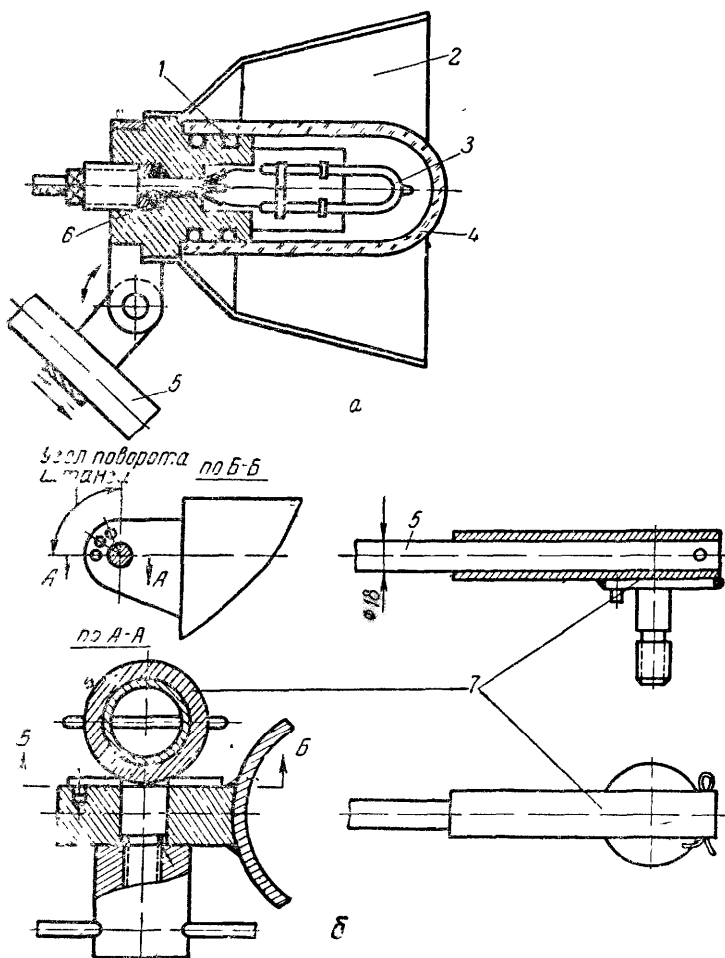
а и б: 1 — резиновые кольца; 2 — рефлектор; 3 — лампа-вспышка; 4 — колпачок из оргстекла; 5 — штанга; 6 — резиновая прокладка; 7 — втулка подвижная
